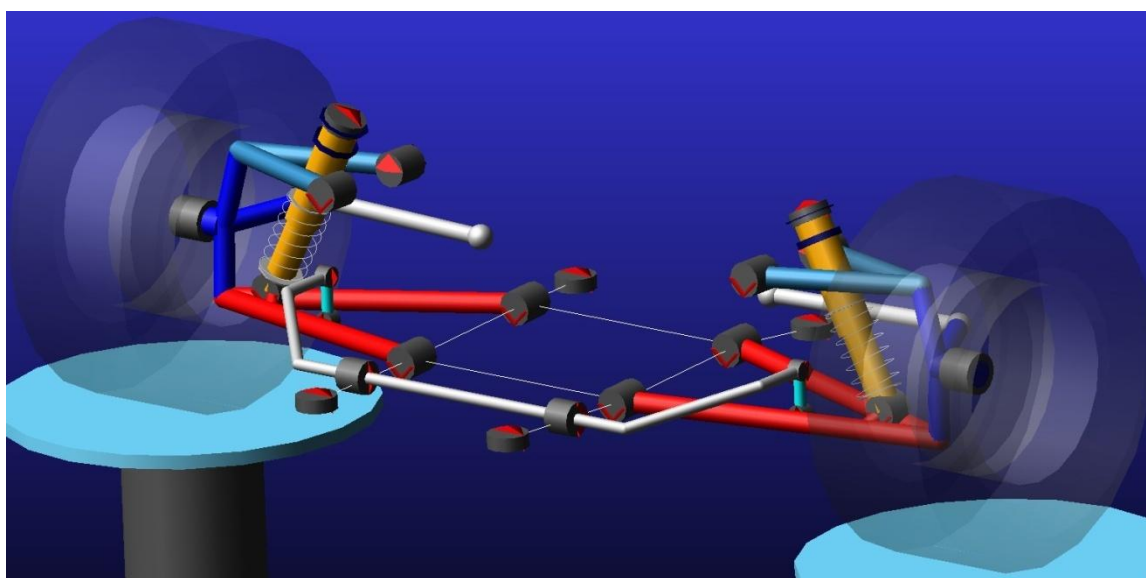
Drátový parametrický model s detailem na levou stranu stabilizátoru
